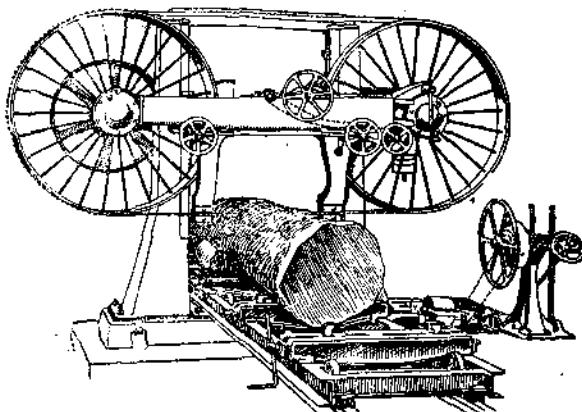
Горизонтальный станок с ленточной пилой для распиловки краев.
